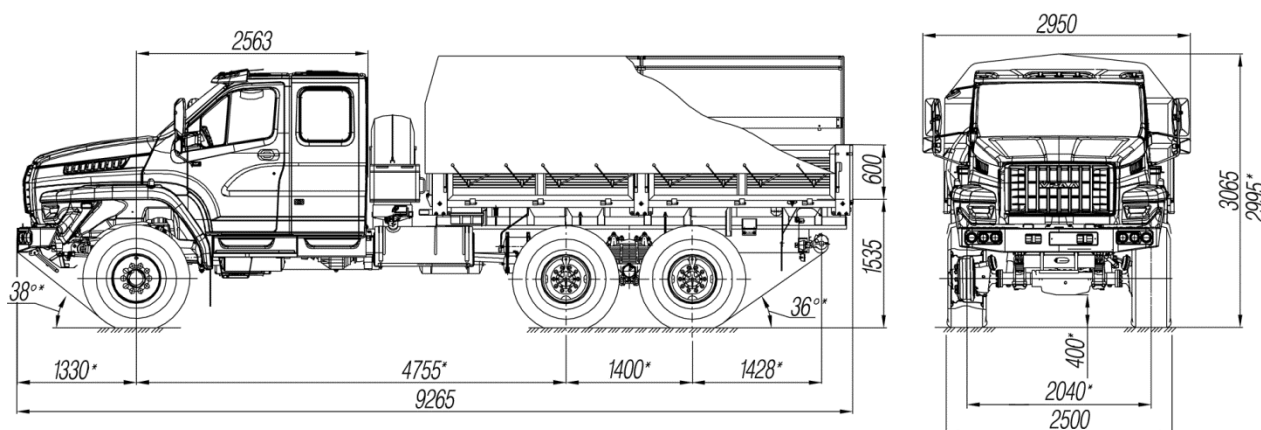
Габаритные размеры автомобиля Урал-4320-5982-72/74
